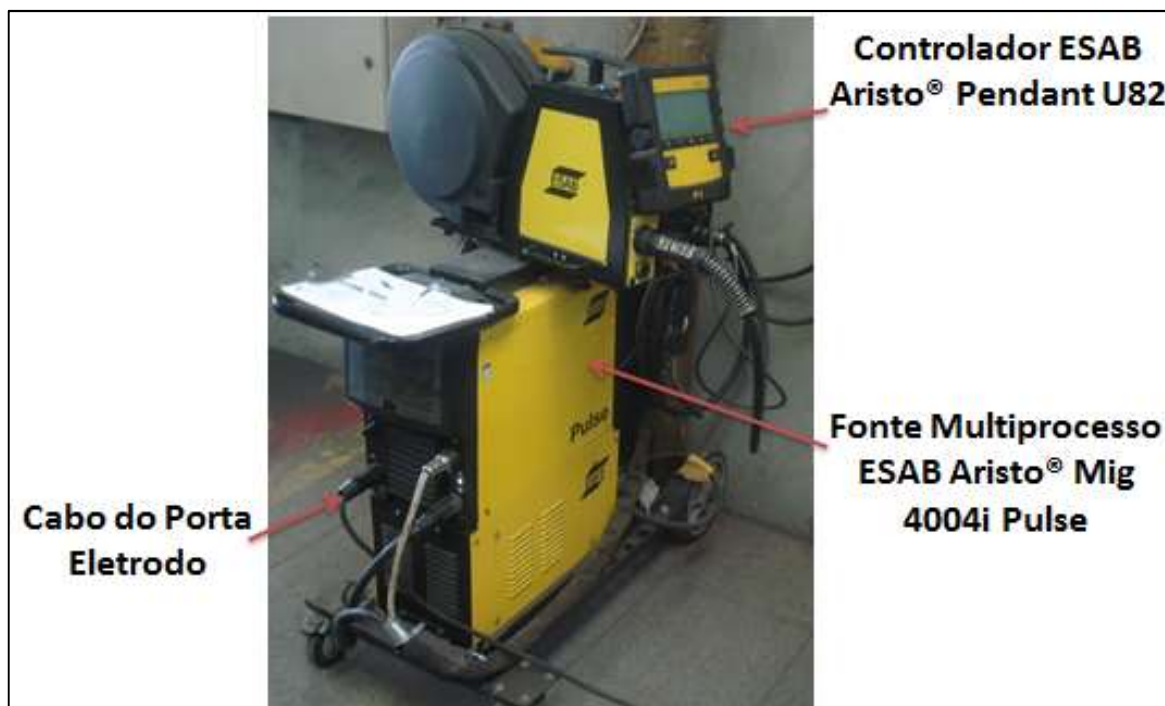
Equipamento utilizado para soldagem dos corpos de prova.
